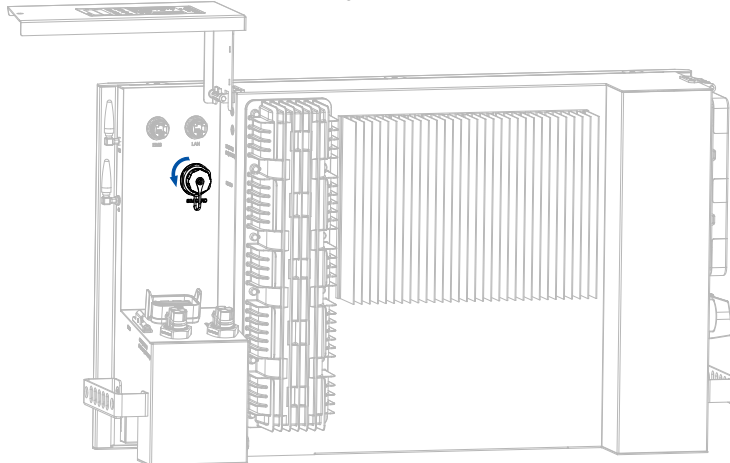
Desserrage du couvercle du logement pour carte SIM
